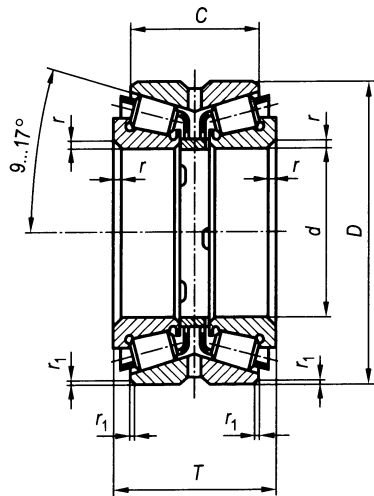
Подшипник роликовый радиально-упорный конический двухрядный
